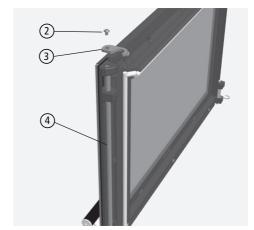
Poignée de porte : desserrage de l'axe de poignée
